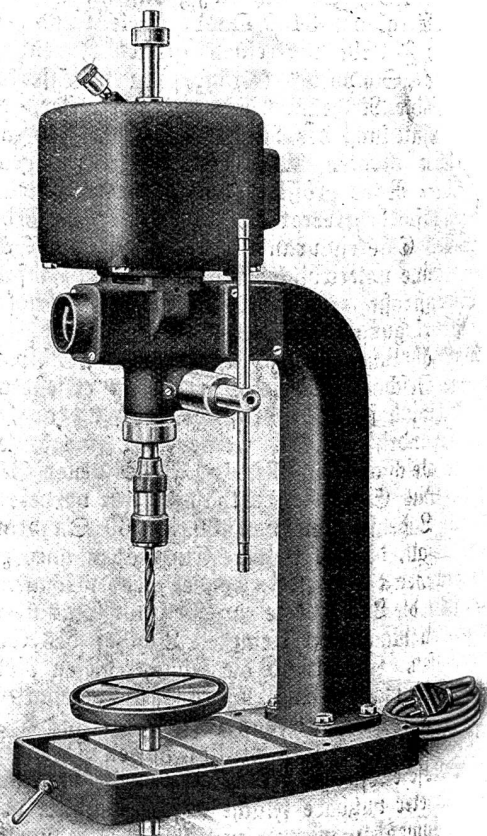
, Bohrmaschine mit direktem Motorantrieb (Werkzeugmaschinenbau)
